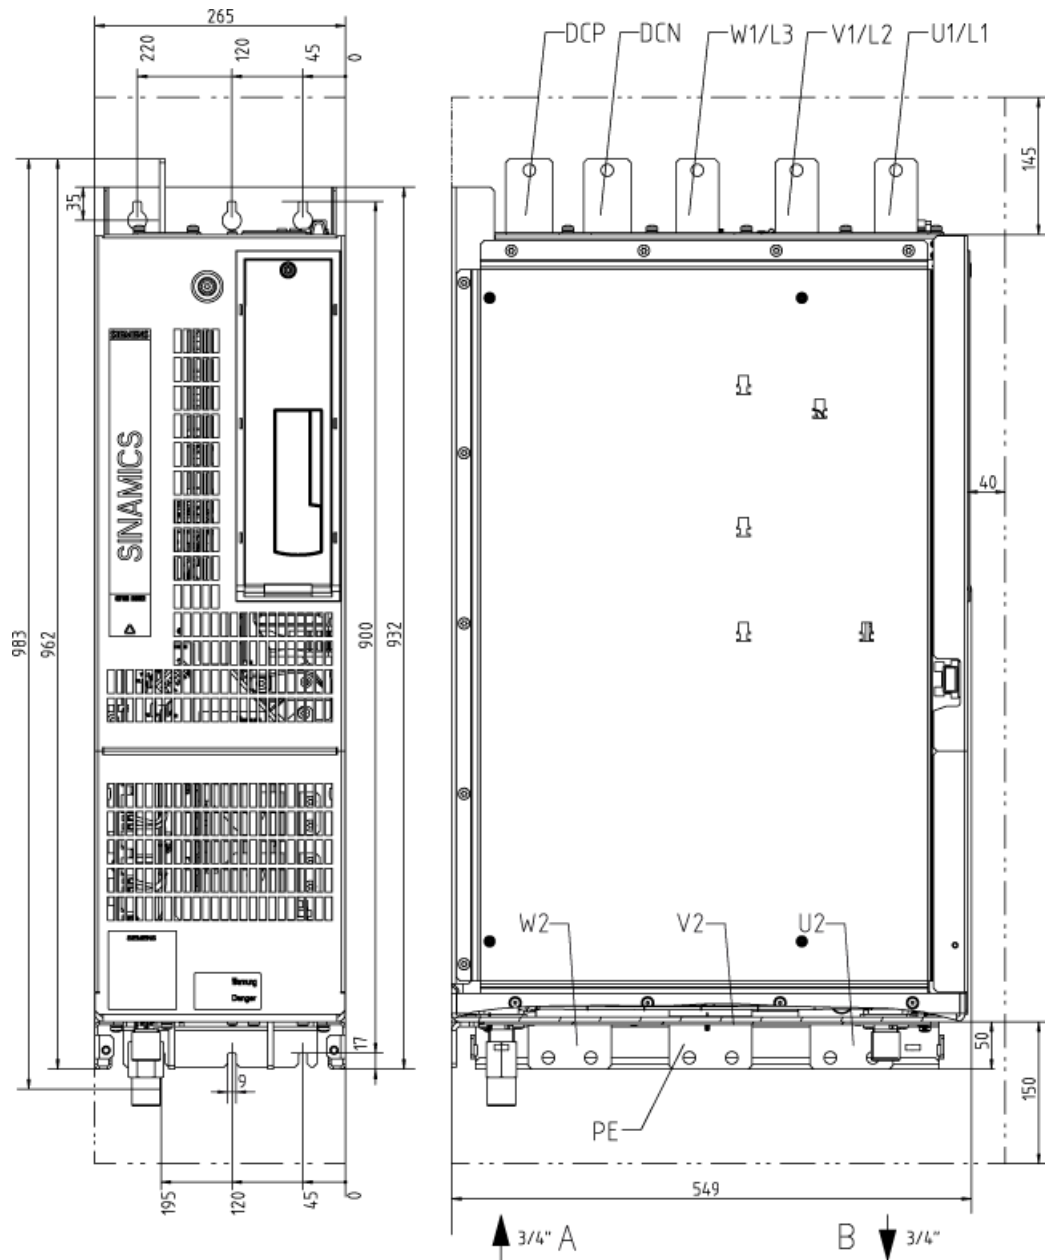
Габаритный чертёж силового модуля, типоразмер GL. Вид спереди, вид сбоку
